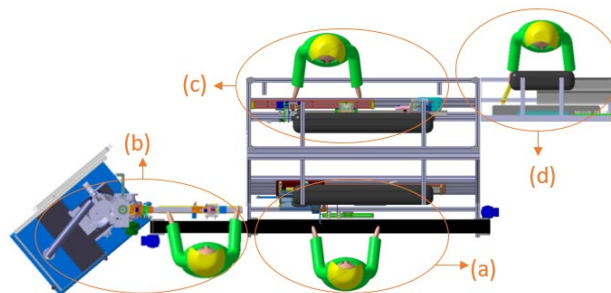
Linha de montagem Transit Exteriores; (a) – Posto de aparar; (b) – Posto de injeção de zamak; (c) – Posto ensaio de tração; (d) – Posto de etiquetagem
